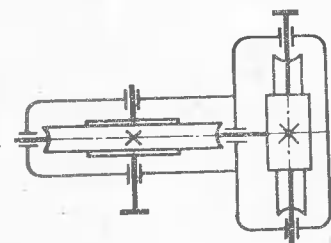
Кинематическая схема одноступенчатого червячного редуктора с нижним расположением червяка
